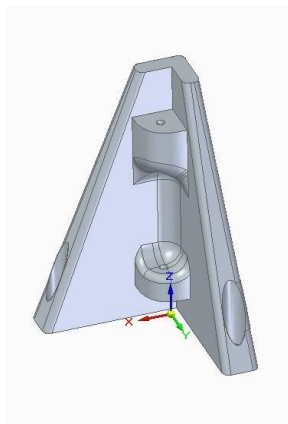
Posicionamento da placa das cargas na estrutura da Jiga de Teste.
